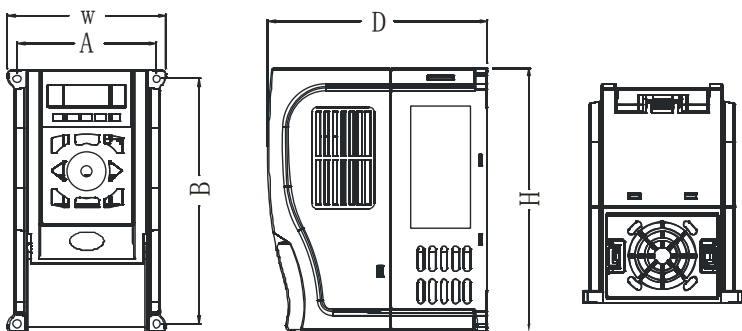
8000系列 塑胶结构外型尺寸及安装尺寸示意图
